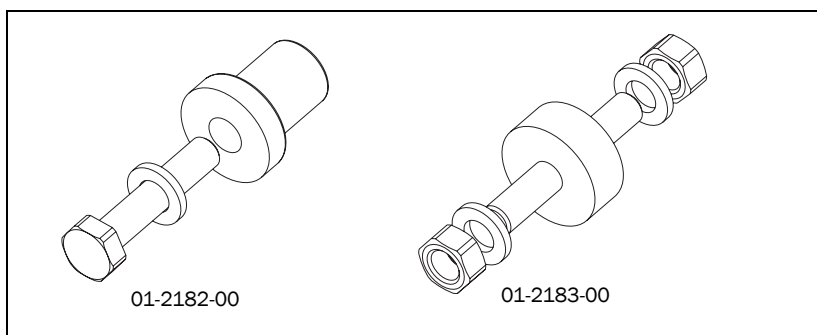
Montagesätze mit Schwingungsdämpfung für den Motor
